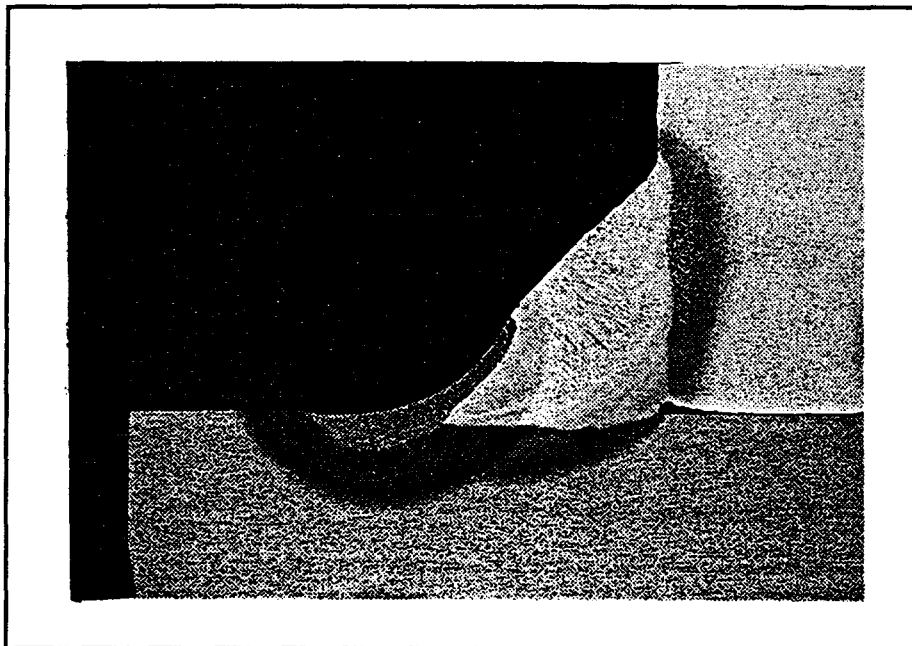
Pied de cordon de soudure refondu à la torche TIG [2]
